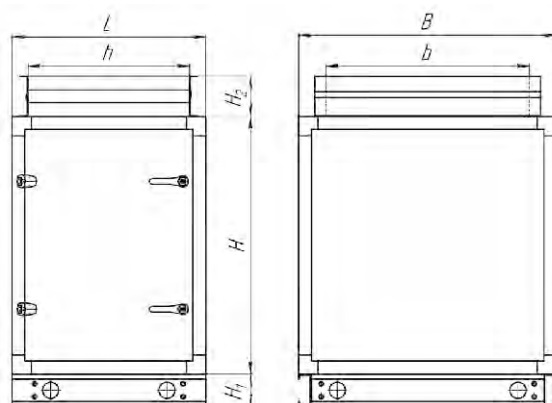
Габаритные и присоединительные размеры. Блок с вертикальным клапаном.
